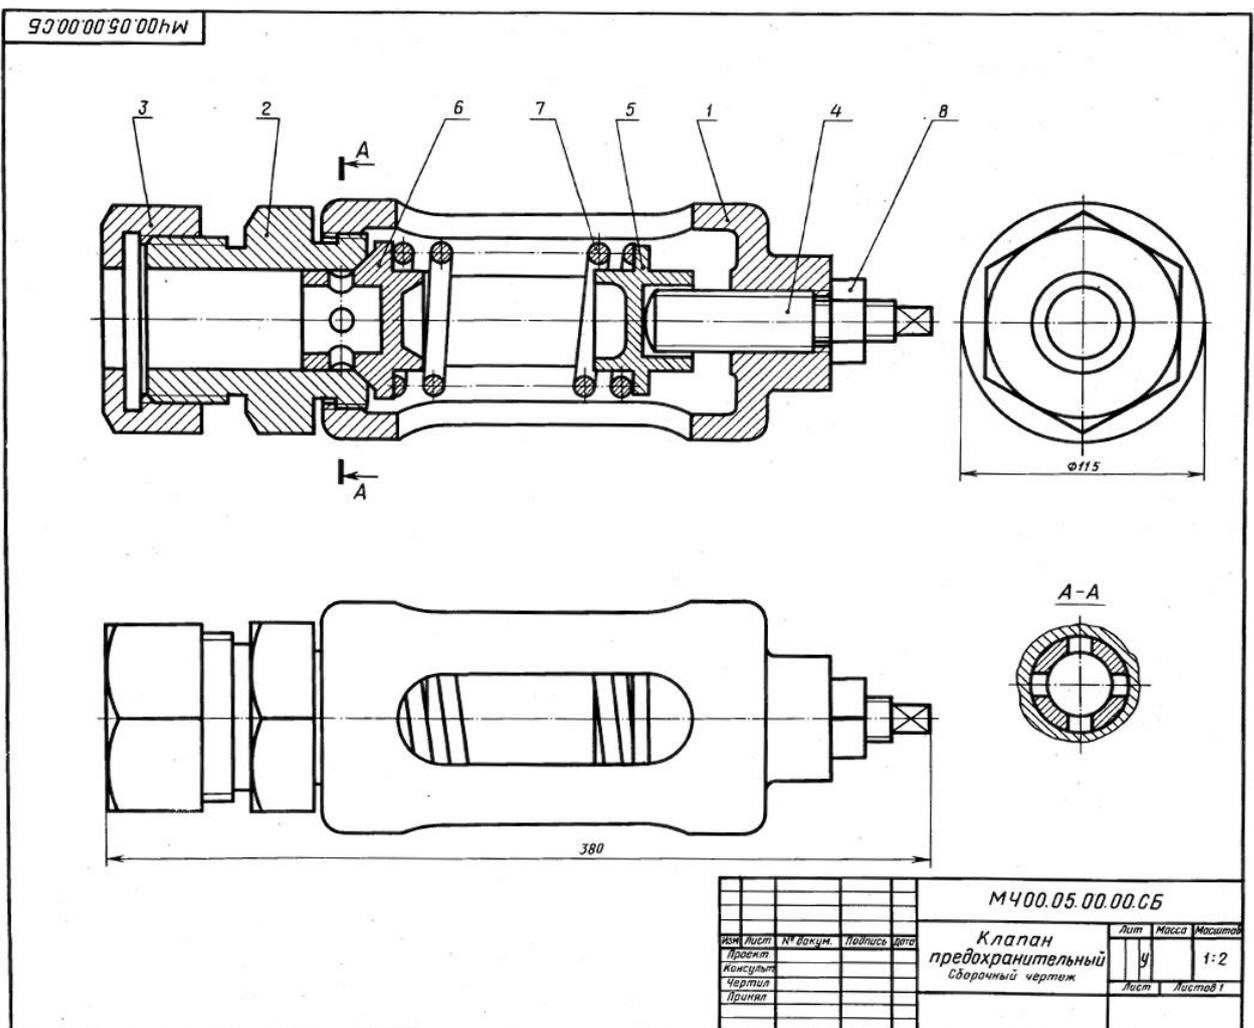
Сборочный чертёж механизма «Клапан предохранительный»
